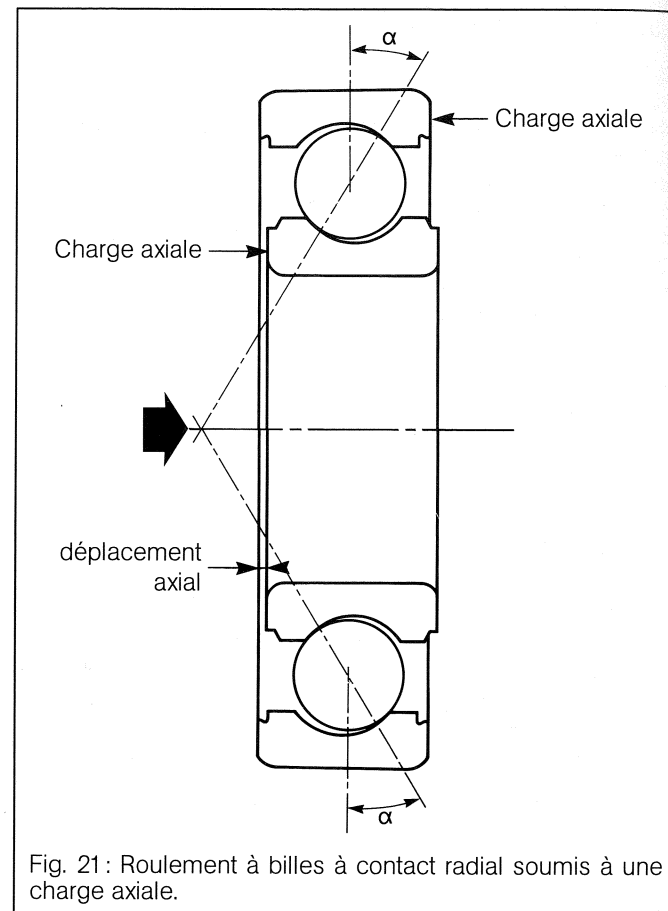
Roulement à billes à contact radial soumis à une charge axiale.
